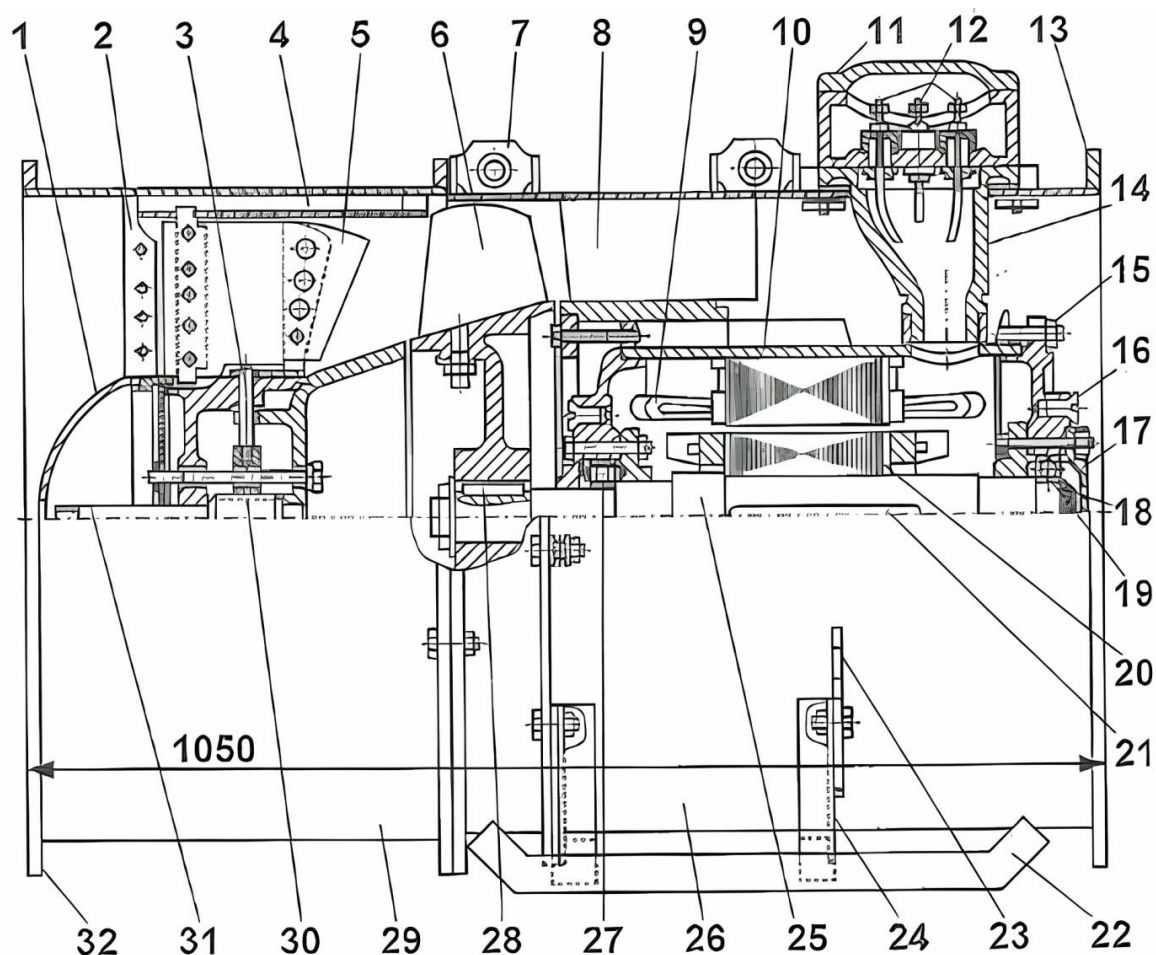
Вентилятор ВМ-6М: 1 – передний обтекатель (кок); 2 – ограждающая решетка; 3, 30 и 31 – привод лопаток направляющего аппарата; 4 – противосрывное устройство; 5 – лопатки направляющего аппарата; 6 – рабочее колесо; 7 – проушина для подвески вентилятора; 8 – лопатки спрямляющего аппарата (опоры для крепления двигателя к корпусу вентилятора); 9 – обмотки возбуждения статора; 10 – оболочка электродвигателя; 11 и 14 – крышка и горловина кабельного ввода; 12 – шпильки двигателя; 13 и 32 – отводящий и подводящий фланцы; 15 – фиксатор; 16 – заглушка; 17 – глухой фланец; 18 – стопорное кольцо; 19 и 27 – задний и передний подшипники; 20 – ротор; 21 и 28 – шпонки ротора и рабочего колеса; 22 – салазки; 23 и 24 – кронштейн и стойка; 26 и 29 – задняя и передняя части корпуса
